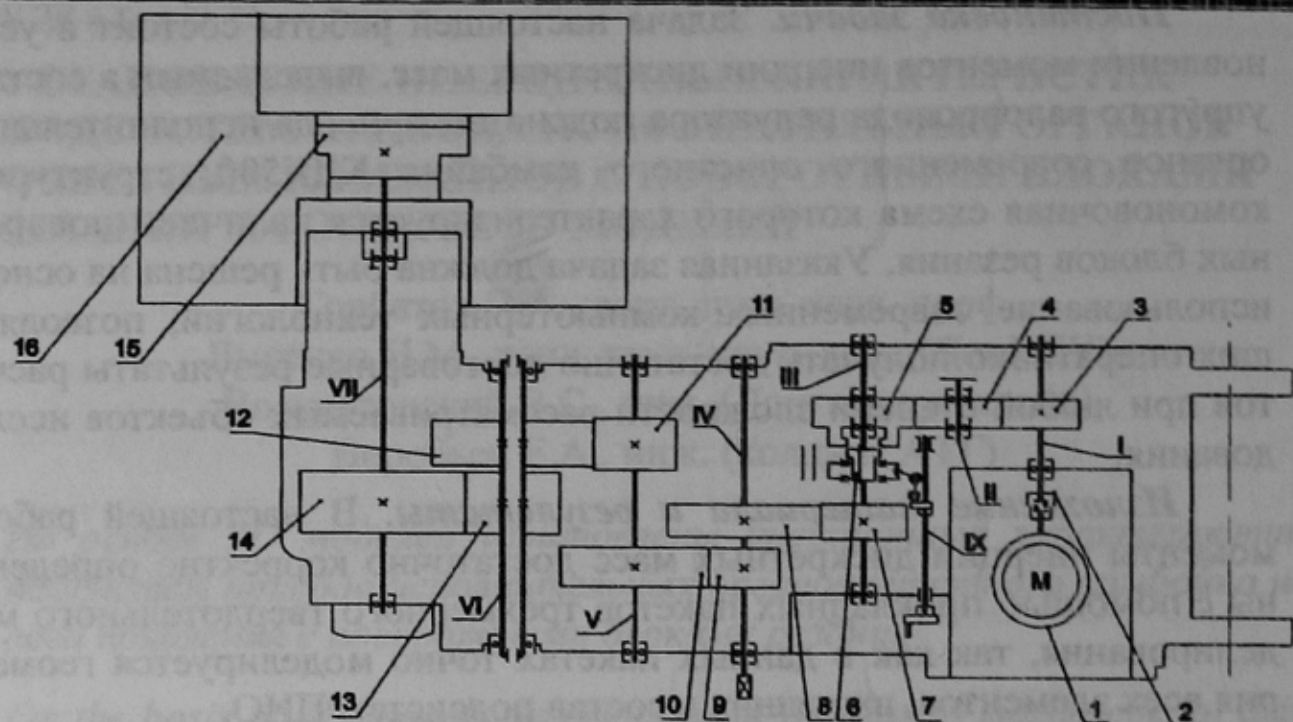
Кинематическая схема редуктора подсистемы привода исполнительного органа комбайна КДК500 I типоразмера
